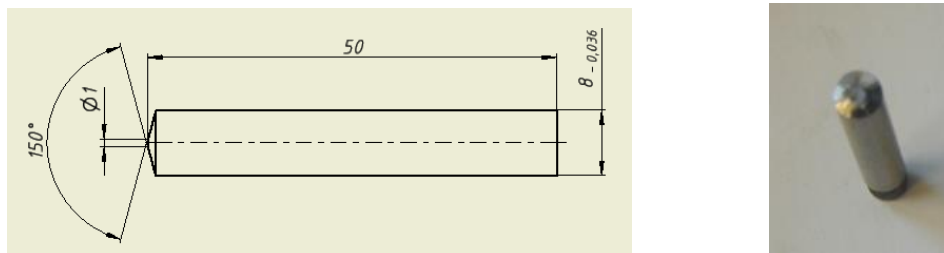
Чертеж (а) и вид (б) индентора из инструментального материала
